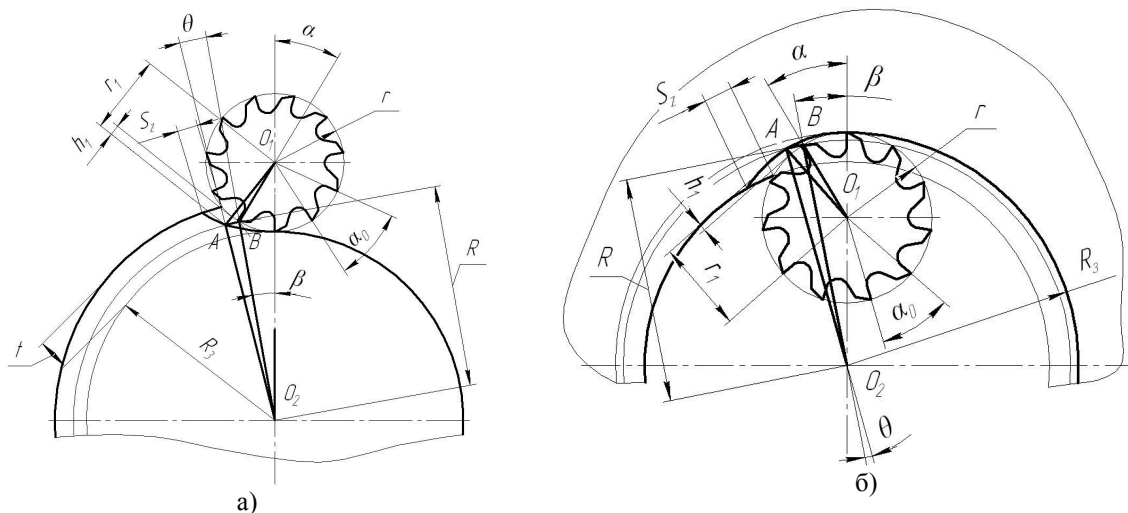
Розрахункова схема процесу фрезерування радіусних криволінійних поверхонь кінцевою фрезою:
